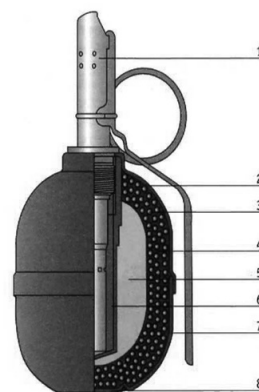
Конструкция польской гранаты RGO-88: 1 — взрыватель (УЗРГМ); 2 — верхняя часть корпуса; 3 — шарики; 4 — пластмасса; 5 — взрывчатое вещество; 6 — втулка; 7 — нижняя часть корпуса; 8 — донушко
